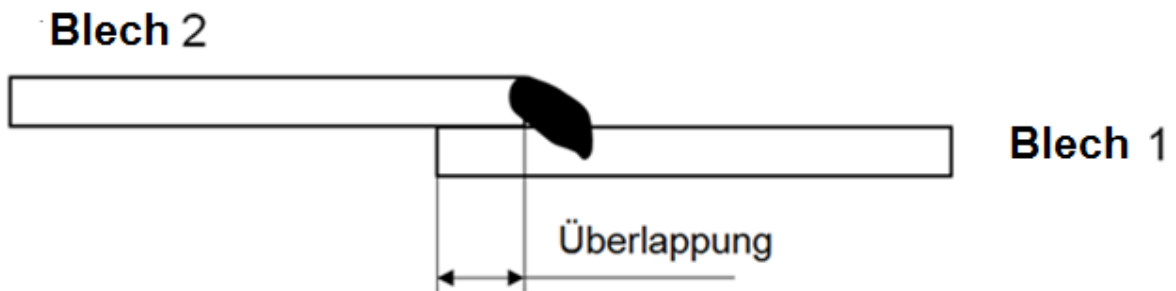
Blechbezeichnungen in der Überlappschweißverbindung
